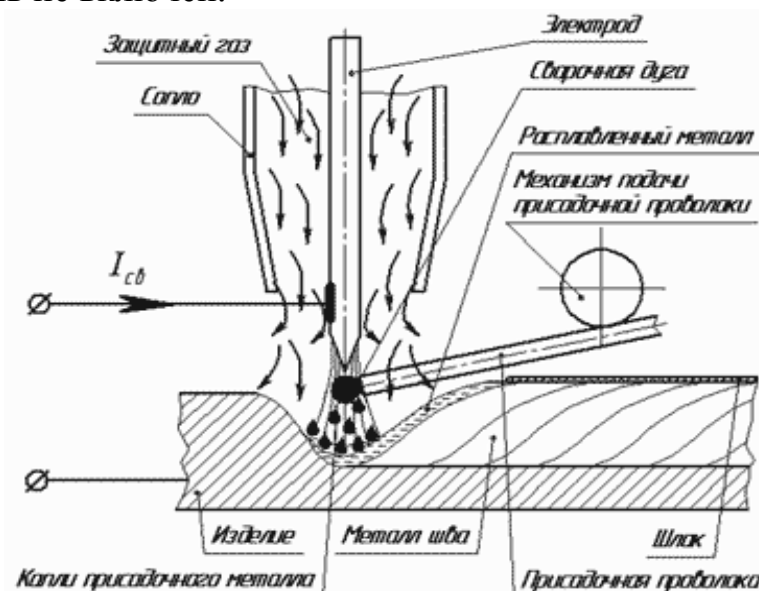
Схема аргонодуговой сварки не плавящимся электродом с дополнительной присадочной проволокой.
